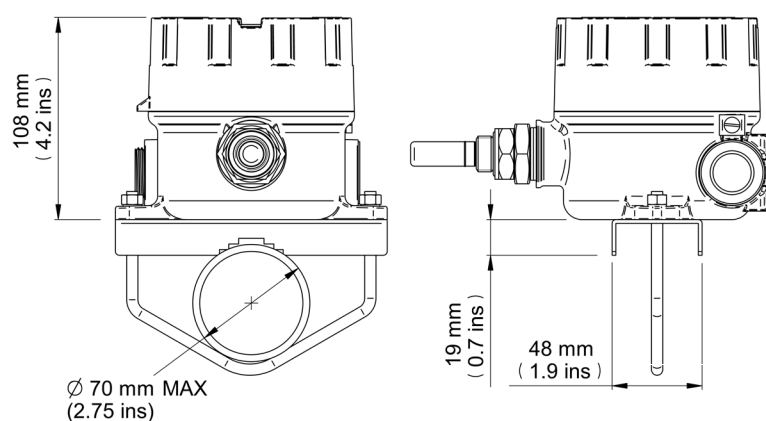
Dimensões Easidew PRO XP EX1 (Sem Display) - Tubulação ou duto
